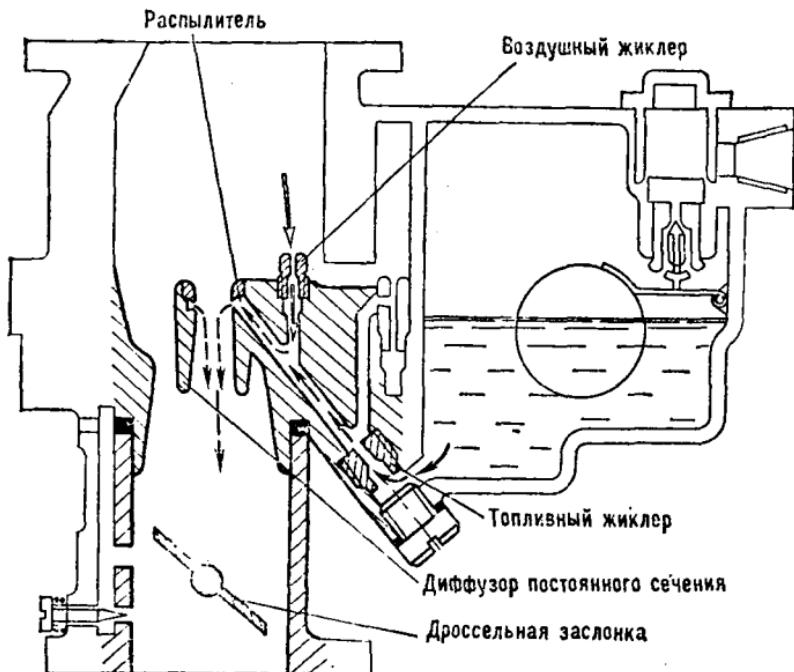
Главная дозирующая система с пневматическим торможением топлива
